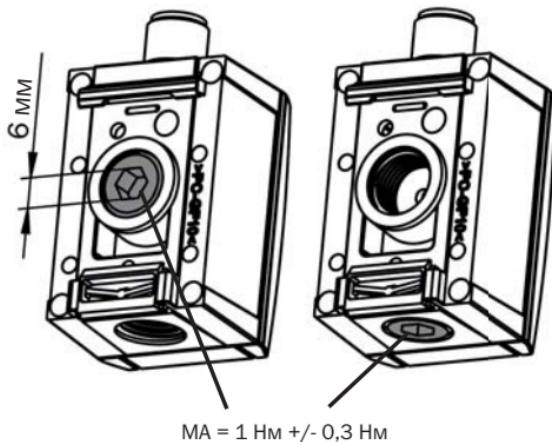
Напорное соединение с внутренней резьбой G 1/4
